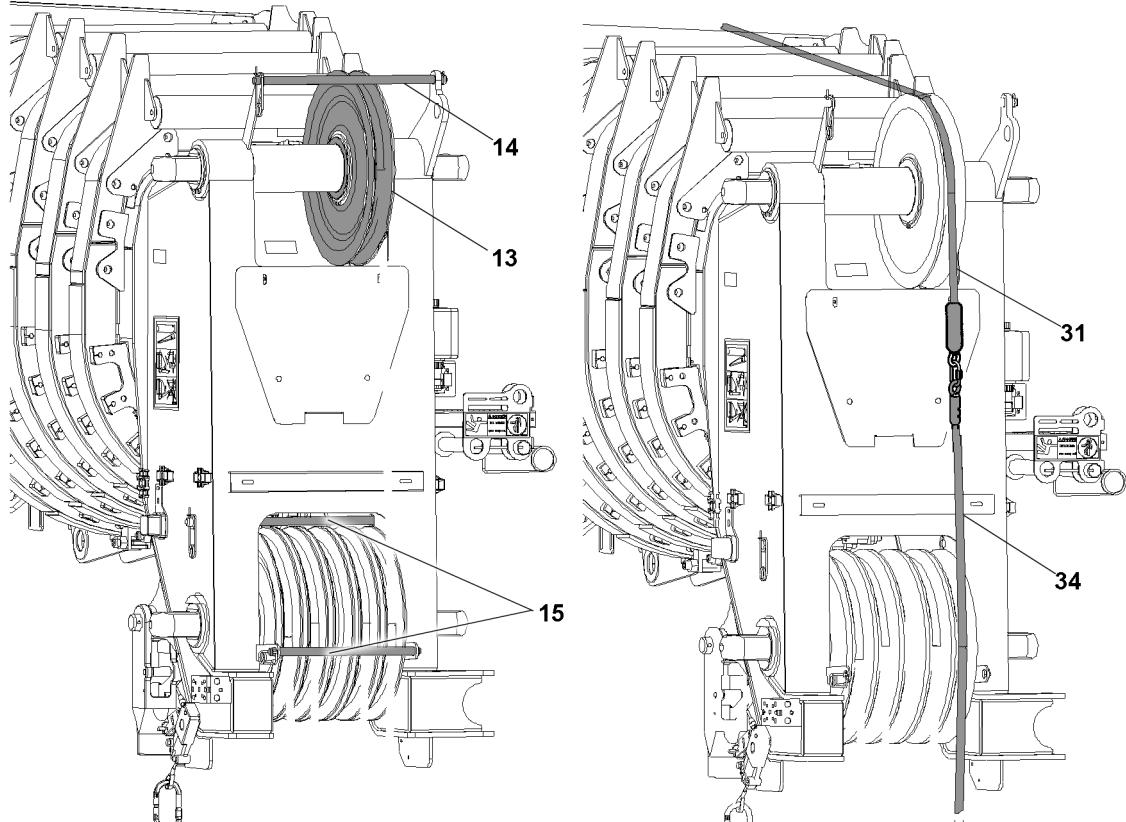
Retirar el cable de elevación con el cable de montaje del cable
